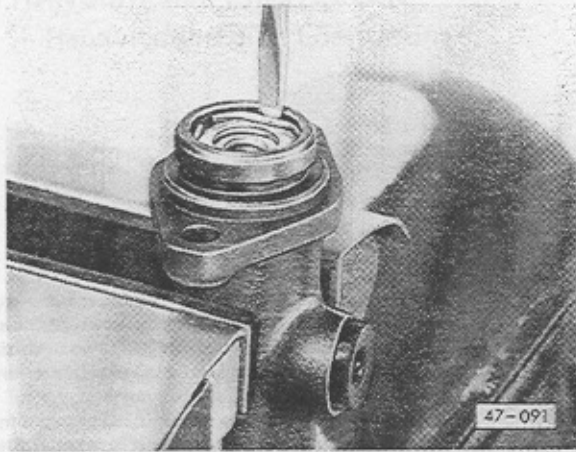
Sicherungsring mit Schraubenzieher heraushebeln
